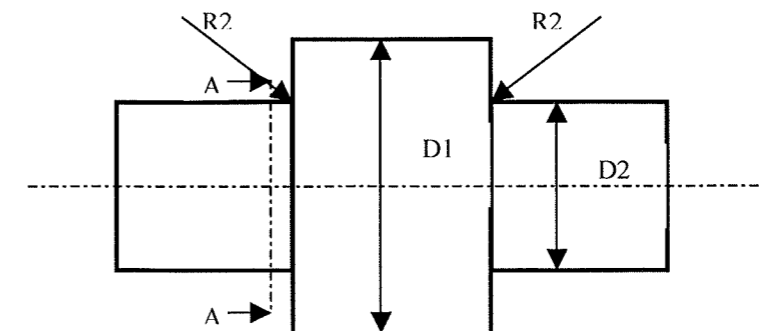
Rappresentazione schematica dell'albero nella sezione di calettamento della puleggia. Misure del raggio in mm.
